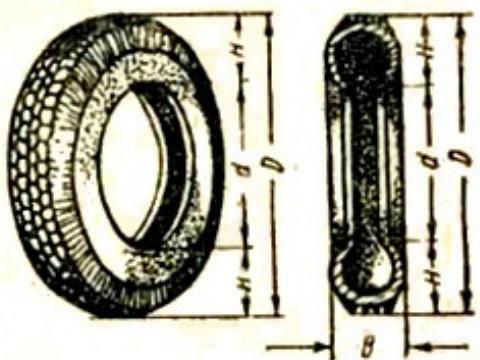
Обозначение размеров покрышки: В - ширина поперечного профиля; Н - высота поперечного сечения; д - внутренний диаметр покрышки или диаметр обода колеса. D - наружный диаметр
